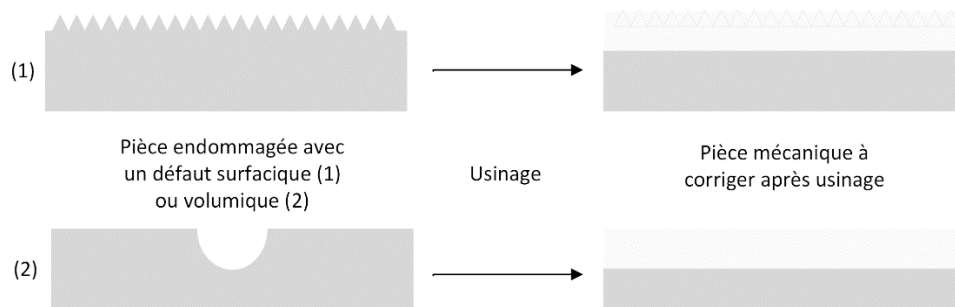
Pièce mécanique à corriger après l'usinage pour la préparation de la surface d'impression
